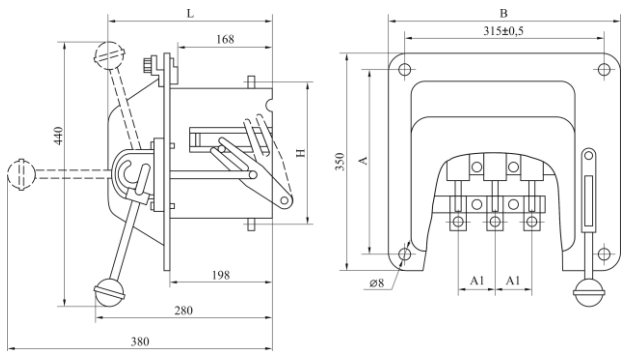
Габаритные и установочные размеры блоков предохранителей-выключателей
